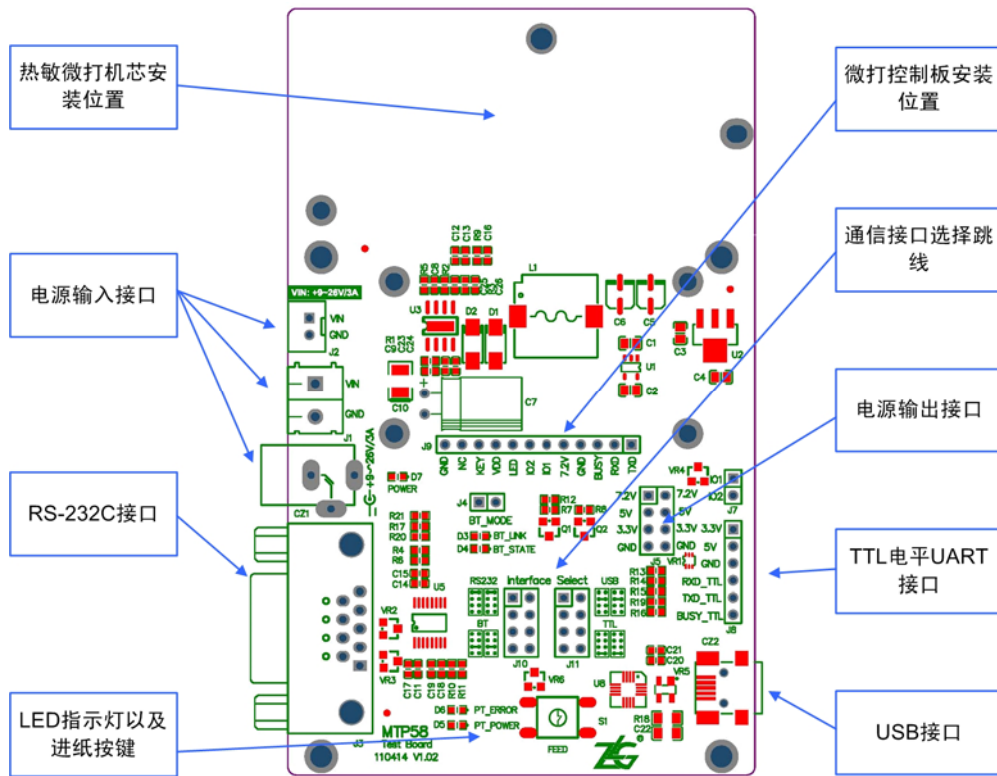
MTP58-FTxx-T1 评估板正面 PCB 丝印
